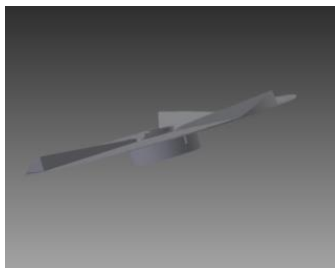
3D-модель лепесткового ротора для обработки Ш. с/п
